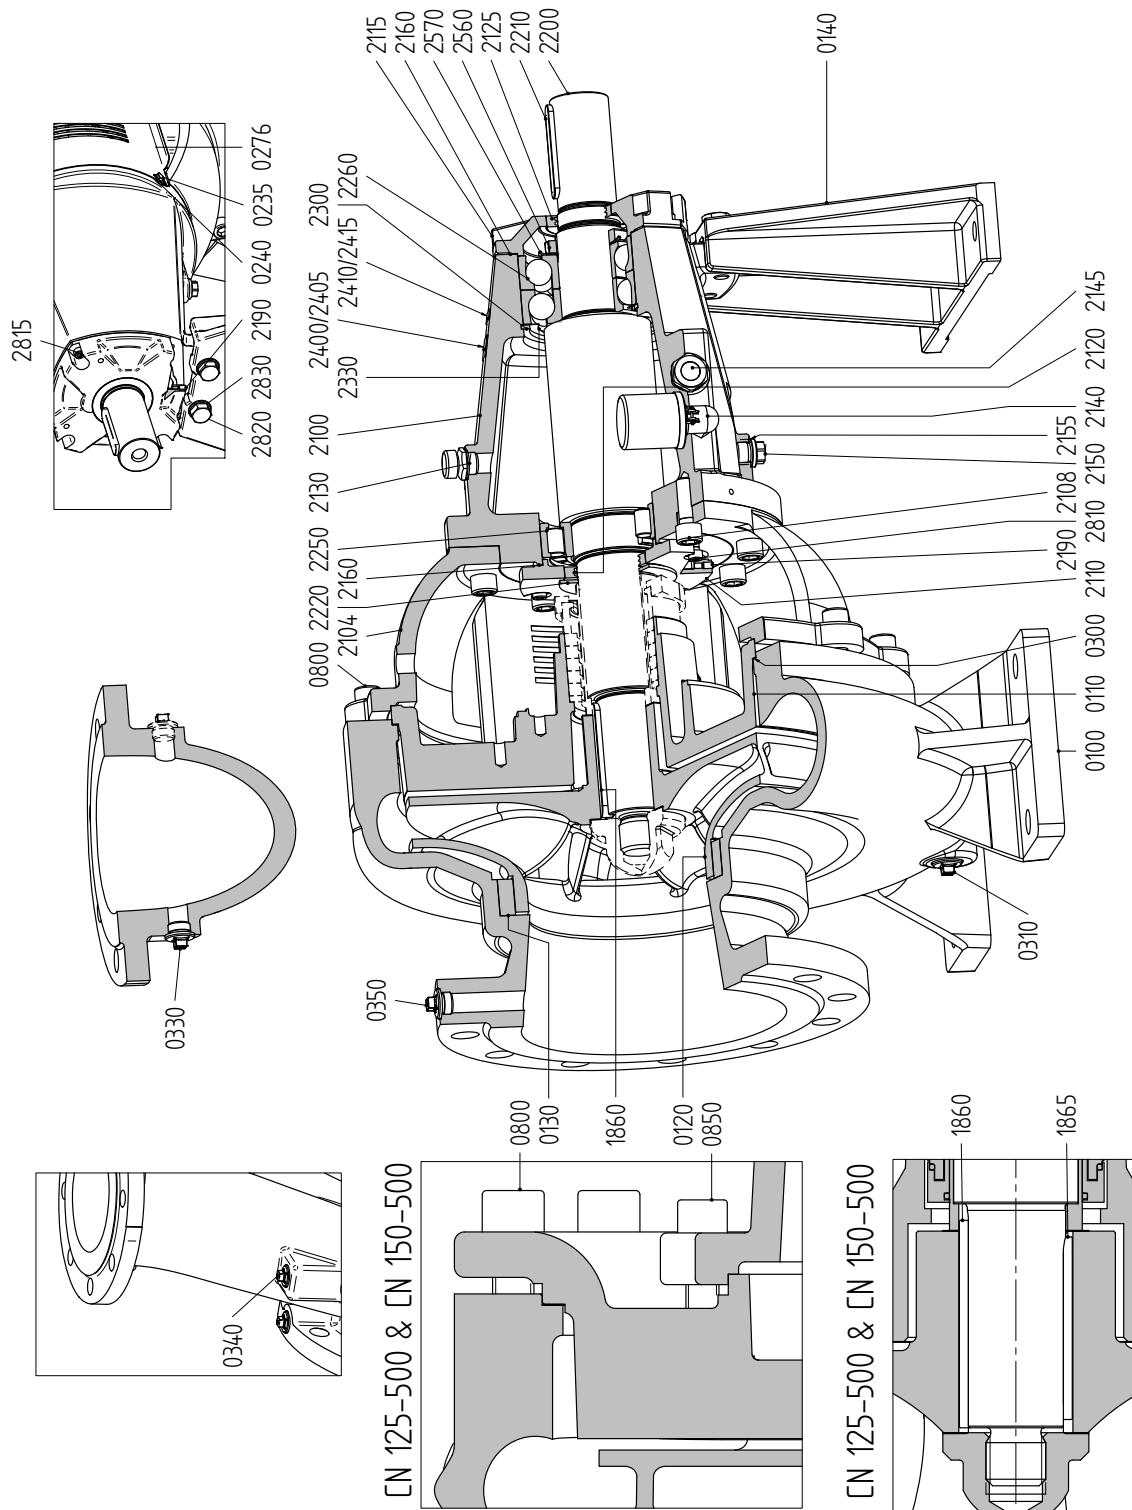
Чертеж в разрезе L4 — группа подшипников 4
